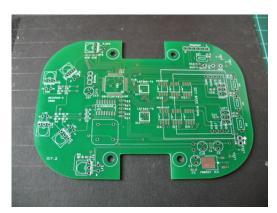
Chasis de un robot de laberinto hecho con PCB
